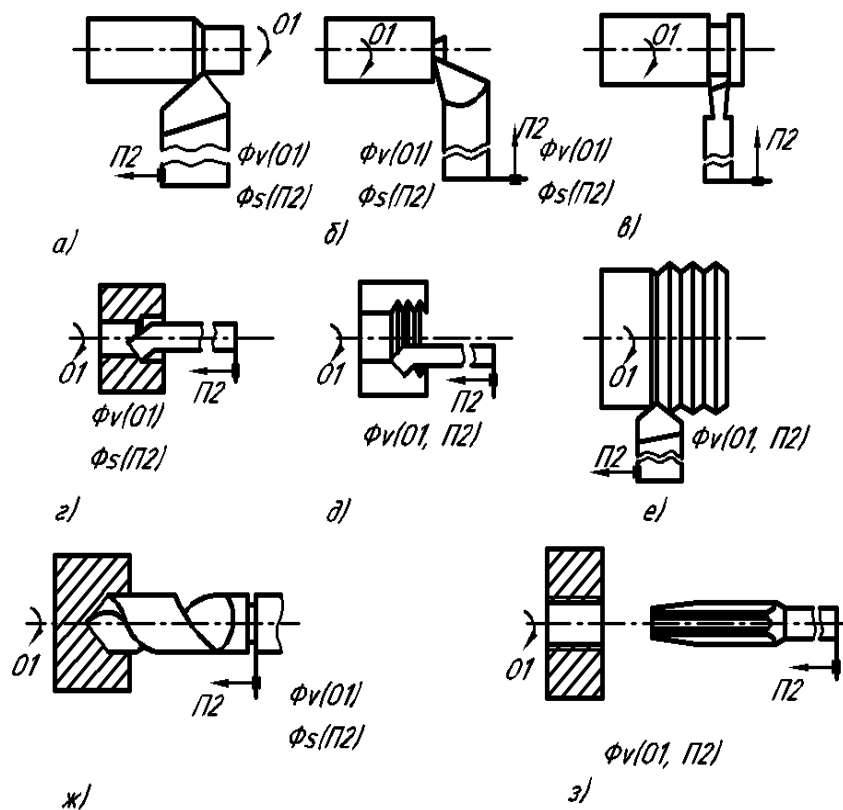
Класичні схеми формоутворення поверхонь на верстатах токарної групи
